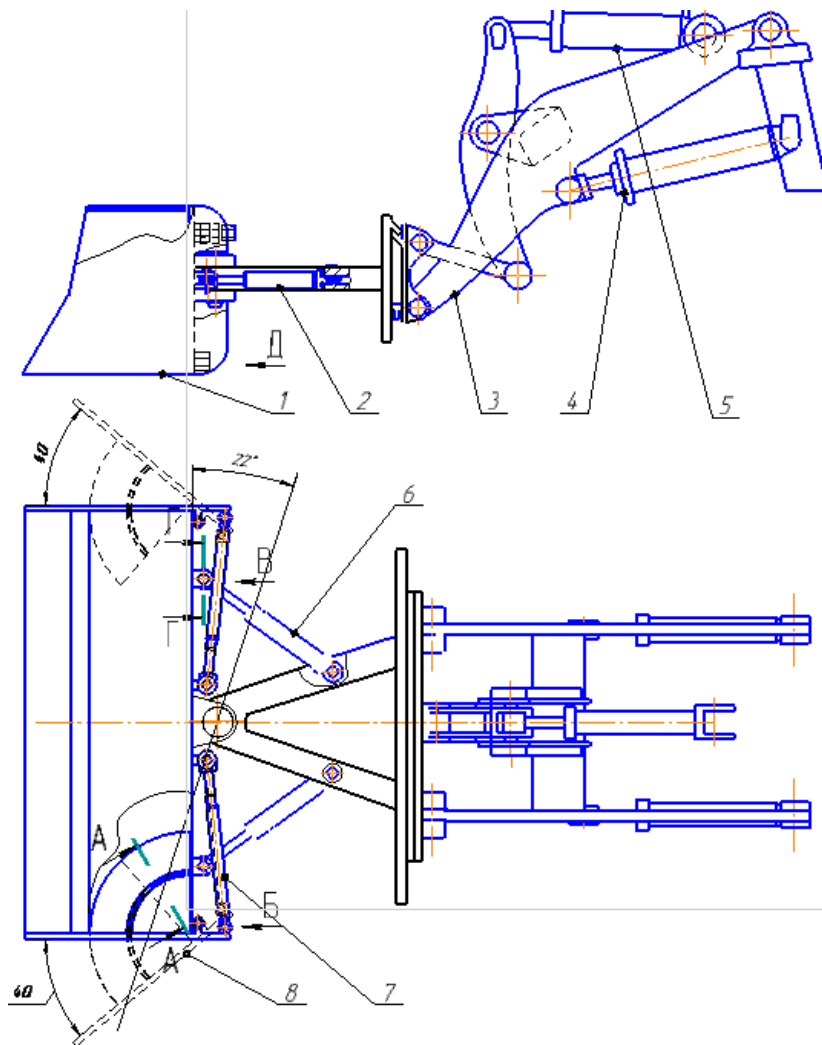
Рабочий орган модернизированного погрузчика Амкодор 332 С4: 1- ковш, 2-рама, 3-стрела,4-гидроцилиндр поворота ковша, 5-гидроцилиндр стрелы, 6-гидроцилиндр поворота ковша в плане, 7- гидроцилиндр боковин
